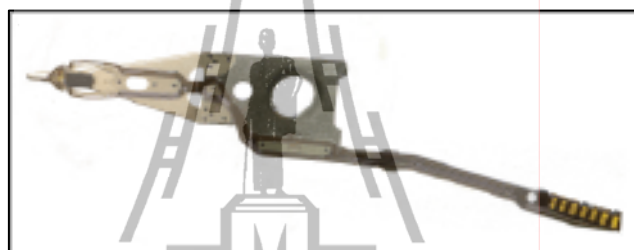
แสดงรูป Head Stack Assembly
